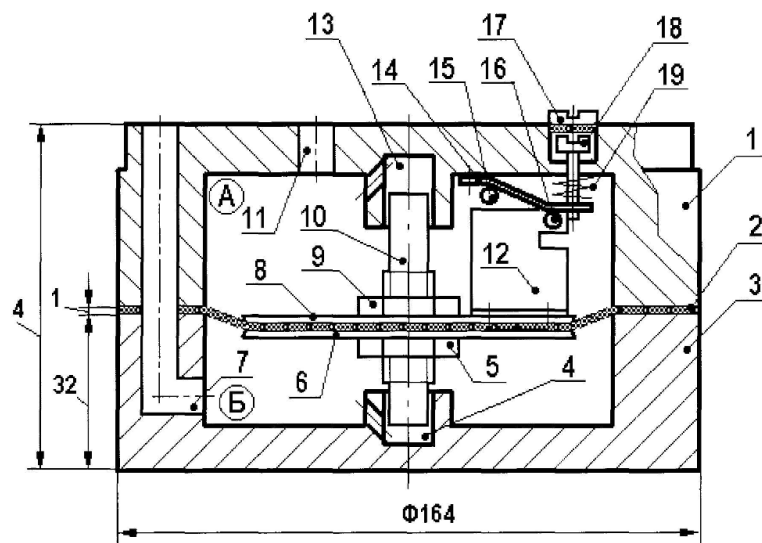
Структурна схема датчика ГРТ: 1 – верхня частина корпусу датчика; 2 – діафрагма; 3 – нижня частина корпусу датчика; 4 - нижня направляюча втулка; 5, 9 – гайка; 6, 8 – шайба; 7 – канал порожнини Б; 10 – стрижень; 11 – канал порожнини; 12 – прапорець; 13 – верхня напрямна втулка; 14 – вилка кріплення пристрою тарування; 15 – перша оптичара; 16 – друга оптичара; 17 – пробка з ущільнюючою прокладкою; 18 – тарувальний гвинт; 19 – пружина
